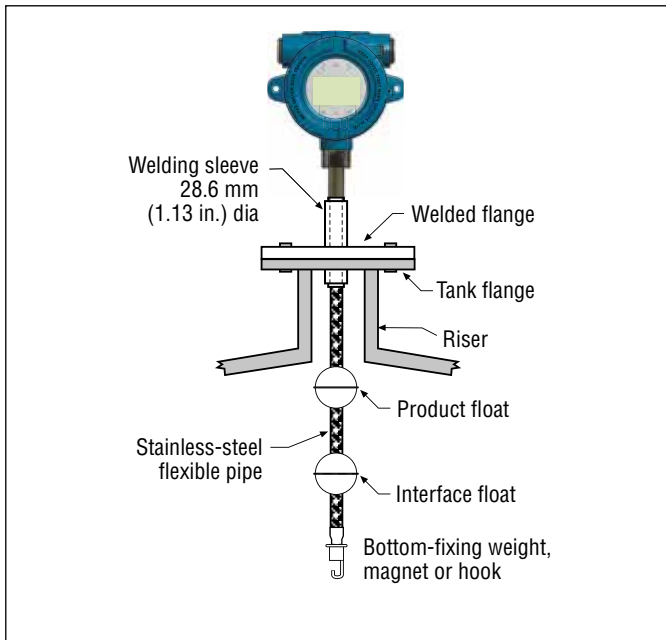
Montage mit Schweißflansch für flexiblen Schlauch
